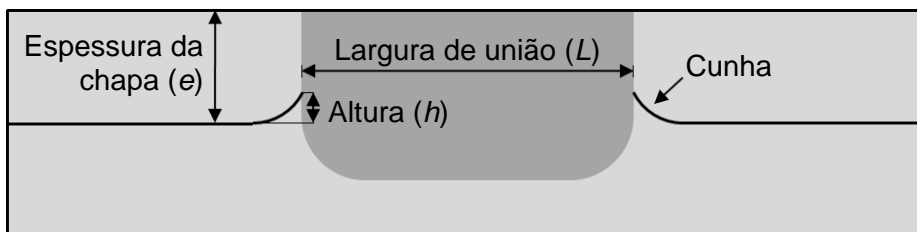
Ilustração esquemática das principais dimensões para avaliação da junta soldada.
